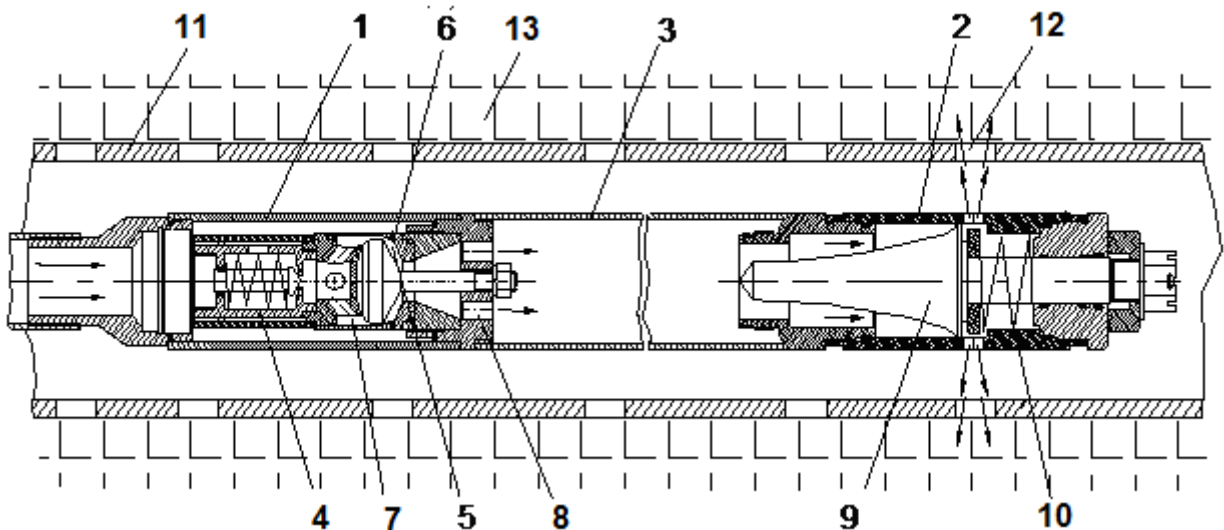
Конструктивна схема генератора коливань та його установка в свердловині.
